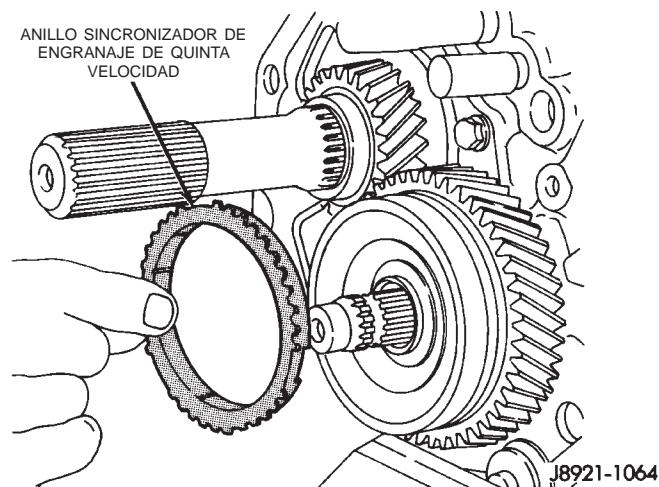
Desmontaje de anillo sincronizador del engranaje de quinta velocidad
